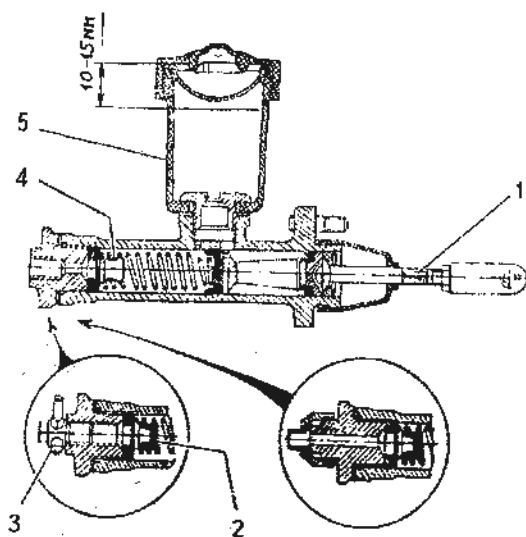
Главный цилиндр тормозов и муфты сцепления:
